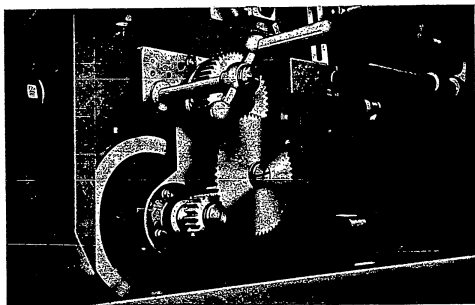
ENGRENAGE D'UN TOUR HP-UT POUR REGLER LA VITESSE DE ROTATION DE L'ARBRE A CAMES
